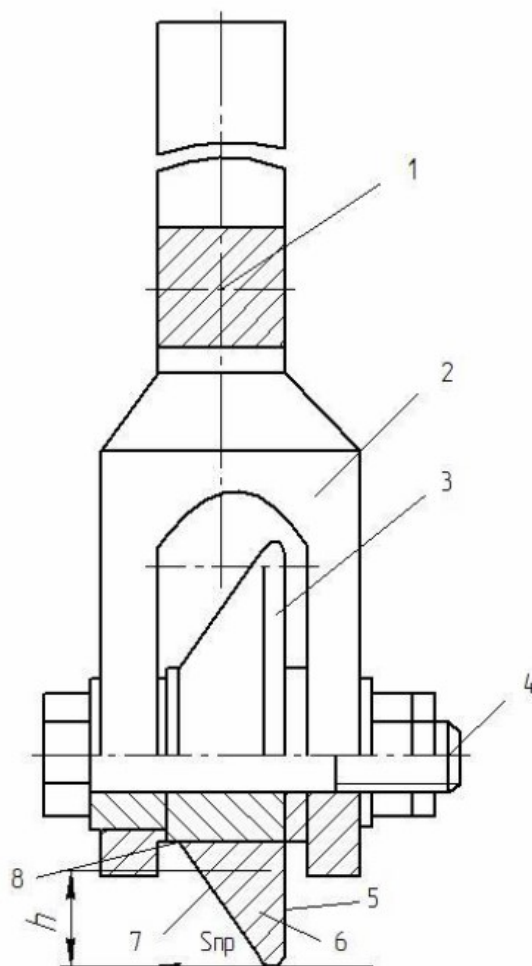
Конструктивні елементи давильного інструменту: 1 - державка; 2 - головка, 3 - давильний ролик, 4 - вісь ролика; 5 - головна задня поверхня; 6 - вершина ролика; 7 - передня поверхня; 8 - підшипник
